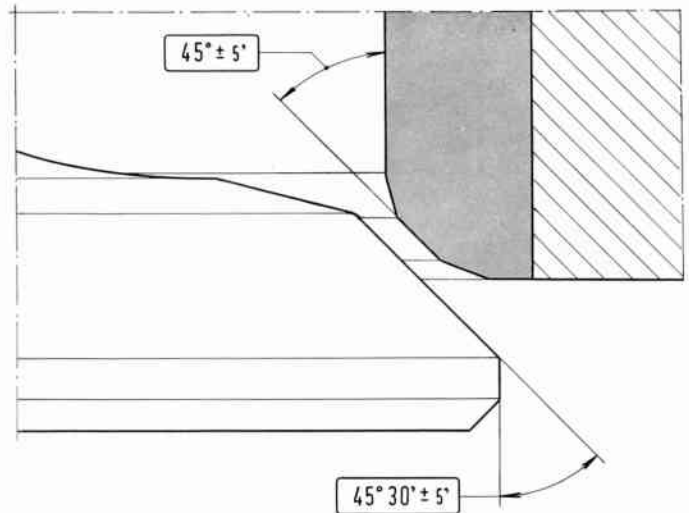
Einpassung des Ventils mit seinem Sitz.
